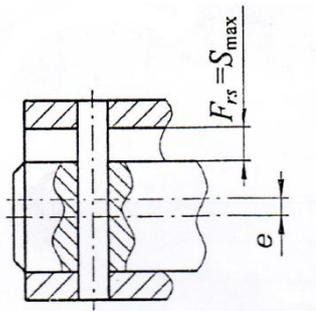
РБЗВ, вызванное максимальным посадочным зазором в соединении колесо - вал.
